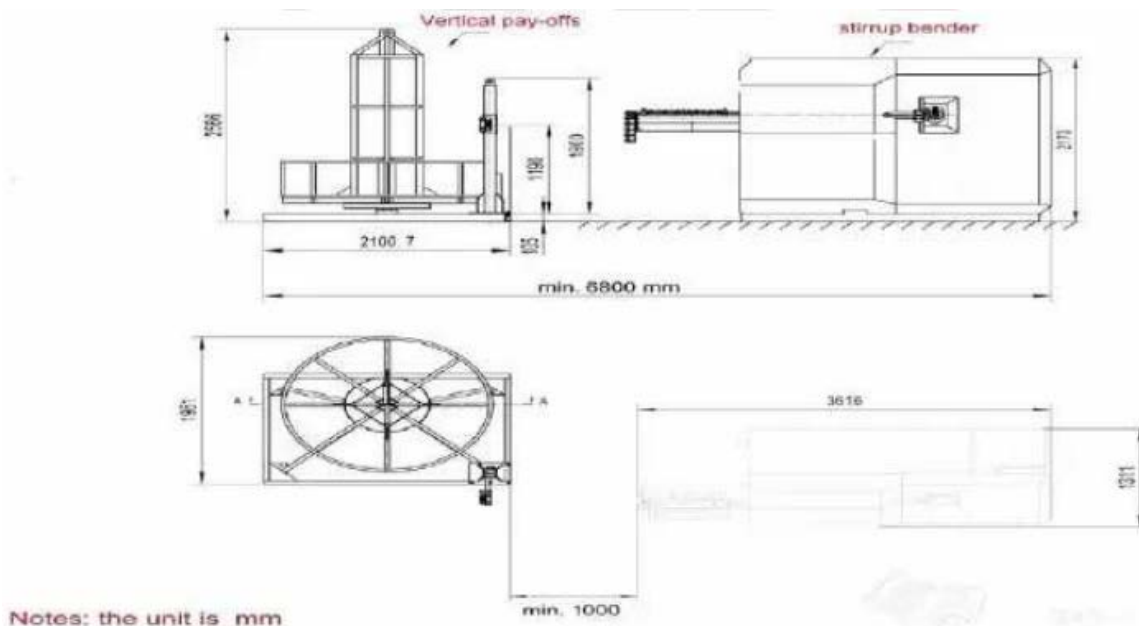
Dimensionnement entre le dévidoir et la machine.[24]
